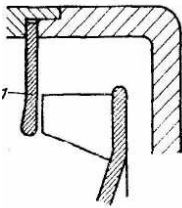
Конструкция вентилятора с неподвижной передней стенкой 1
